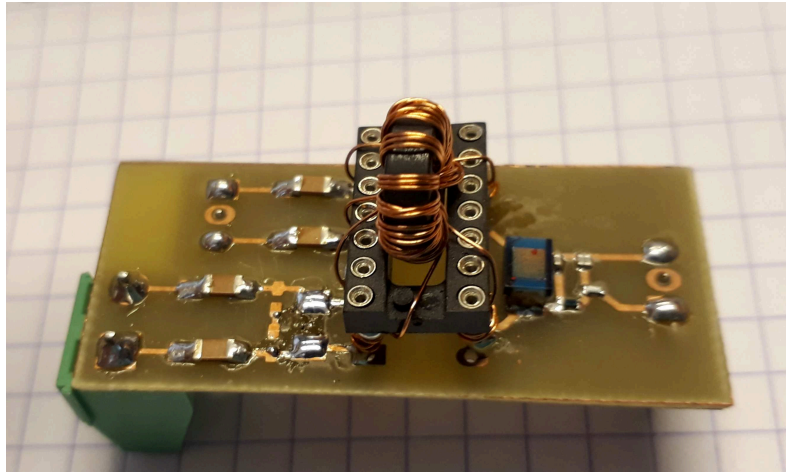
Photographie du PCB réalisé au laboratoire
